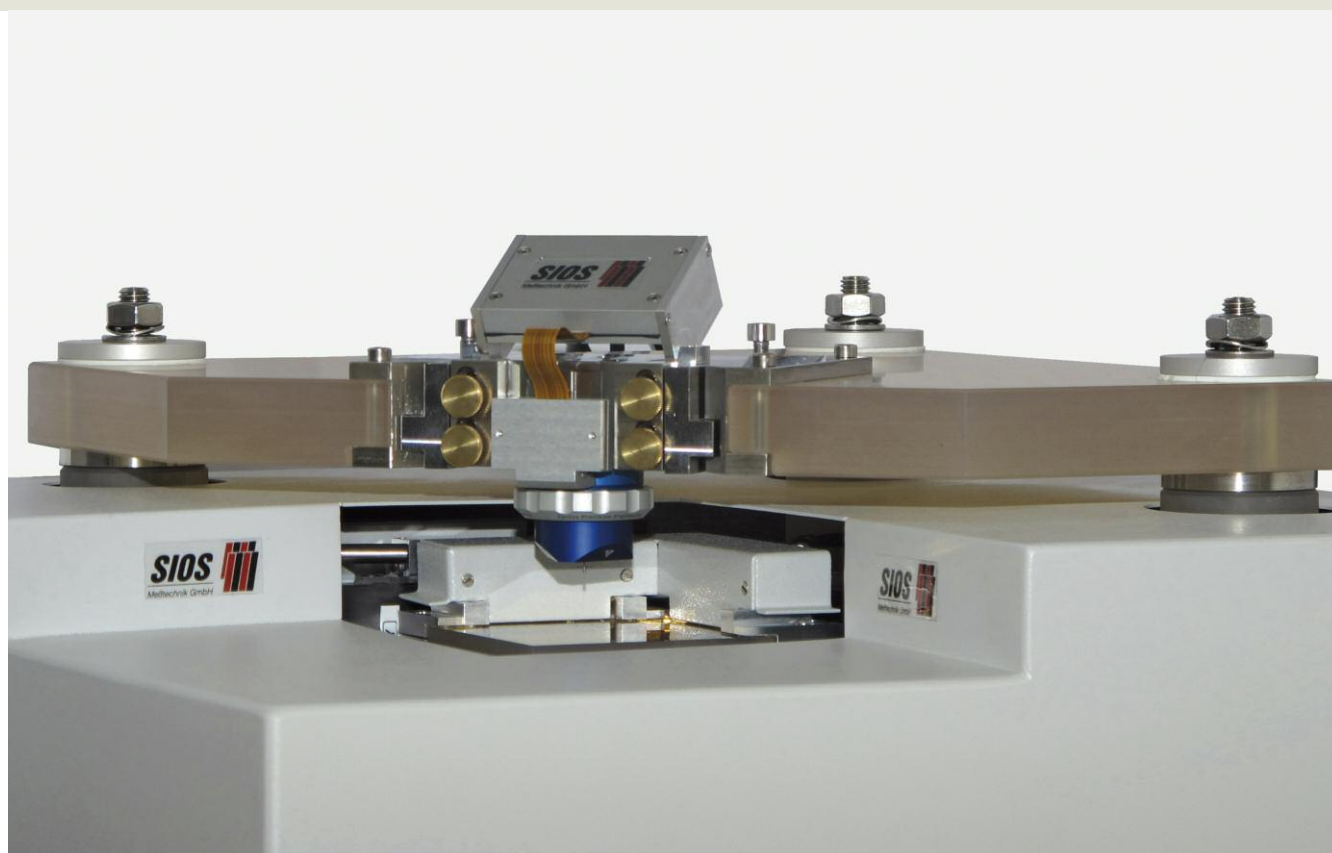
3D-Mikrotaster ›GannenXP‹ der Firma Express Engineering
